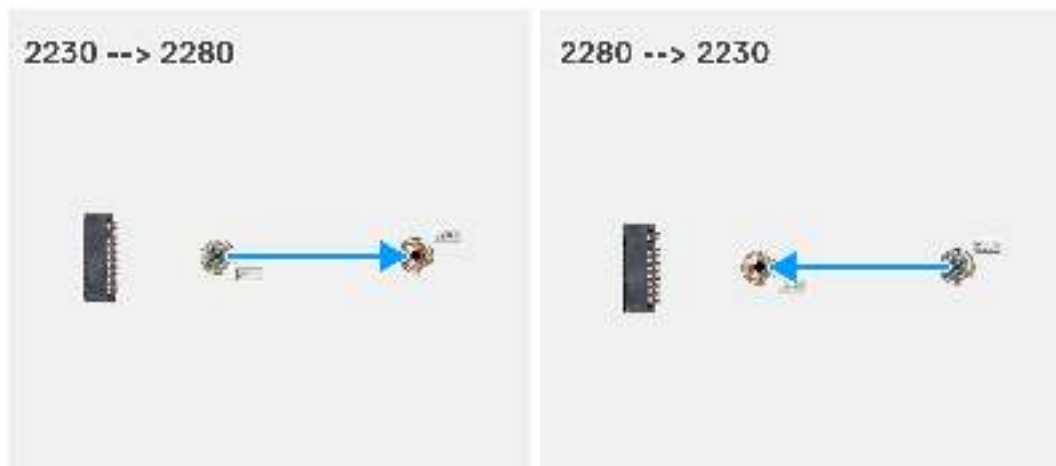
Verschieben der Solid-State-Schraubenhalterung auf M.2-Steckplatz 0
